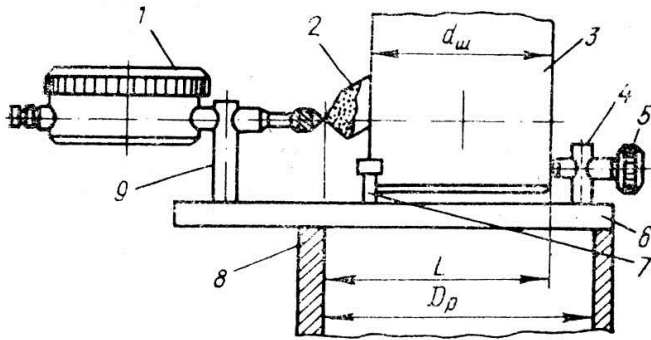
Індикаторний пристрій для встановлення вильоту різця:
